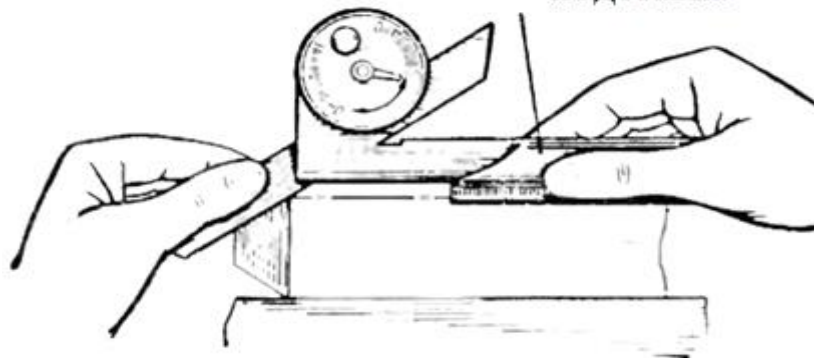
Измерение угла детали, одной из образующихся которого является цилиндрическая поверхность
